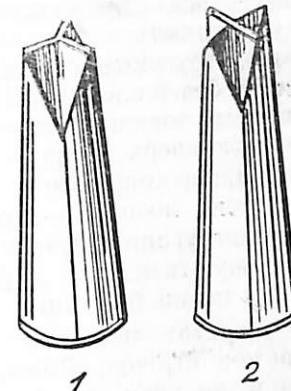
Колунки для розколювання пруття: 1 — трійник; 2 — четверник.
